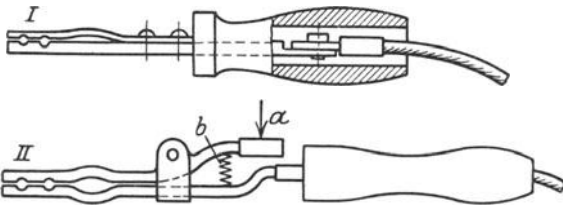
Schweißkolben für Kaltschweißungen.
